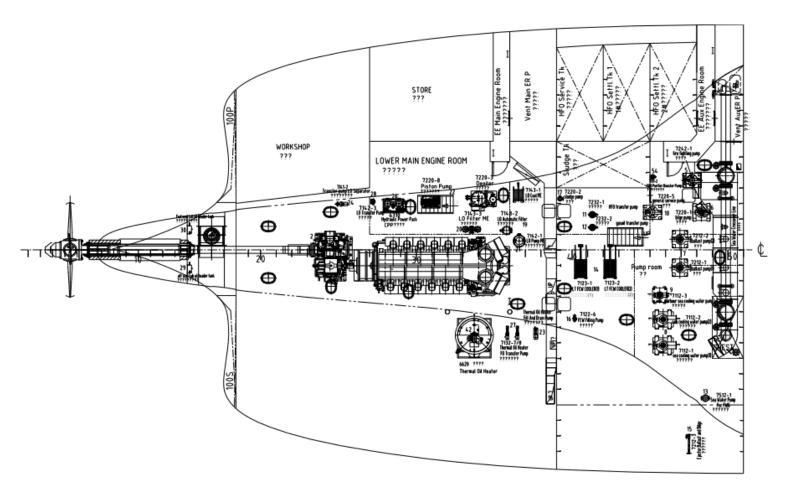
Planta de la sala de máquinas, tecle inferior. Planos del buque.
